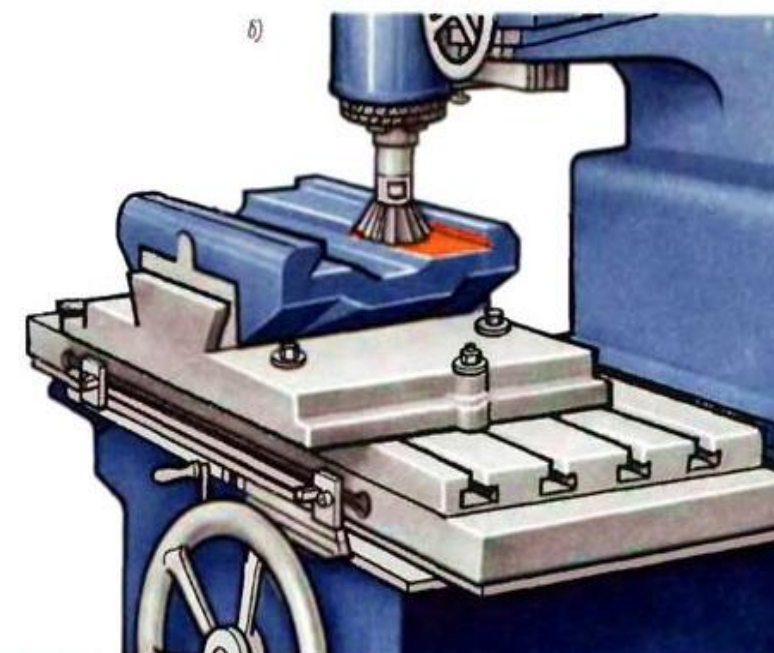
Обработка паза одноугловой концевой фрезой
